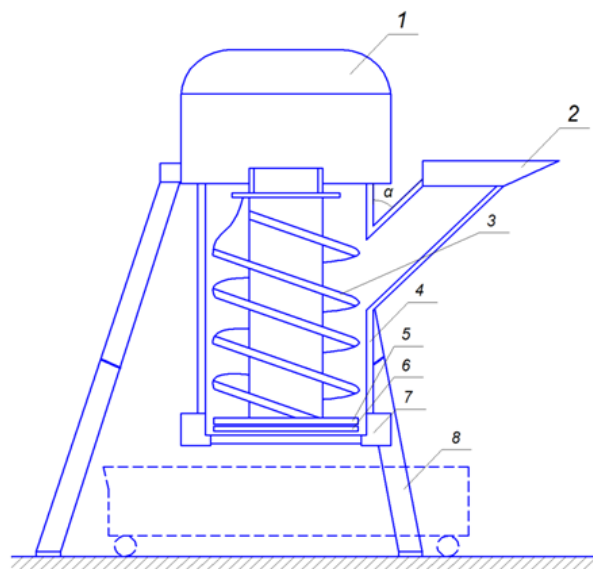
Мясорубка с вертикальным расположением шнека: 1 – корпус; 2 – загрузочная чаша; 3 – шнек; 4 – нож; 5 – решетка; 6 – прижимная гайка; 7 – электродвигатель; 8 – ножки.
